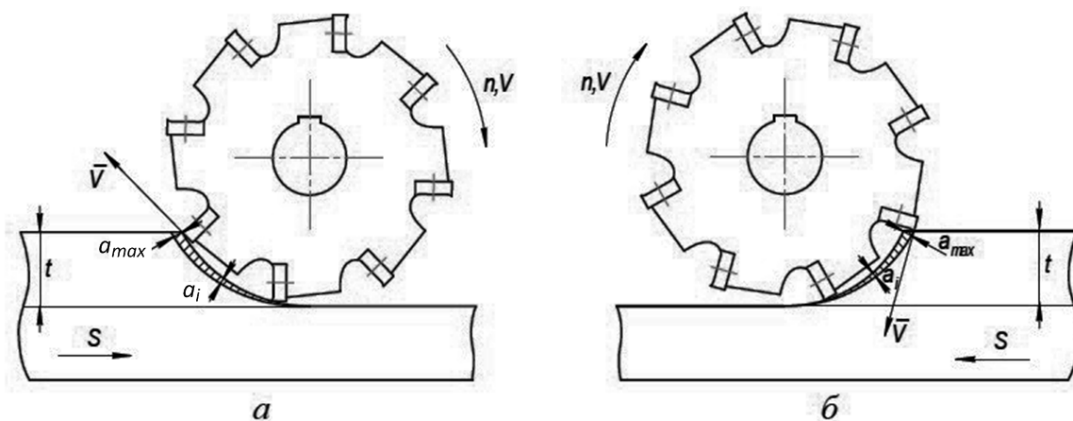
Зустрічне (*a*) і попутне (*б*) фрезерування
